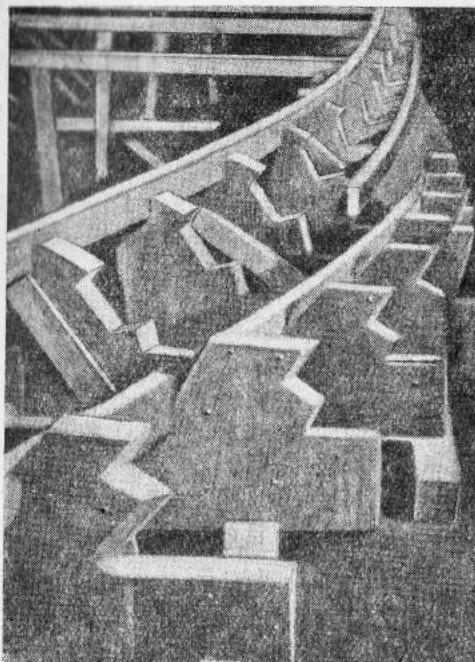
Пресс для склеивания сколовых и привальных брусьев.
